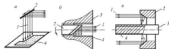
Схемы нагрева изделий под закалку с помощью лазера: а – поверхность цилиндрического изделия; б – внутренняя поверхность отверстия; в – жароустойчивость цилиндрического изделия; 1 – лазерный луч; 2 – маска; 3 – деталь; 4 – зона закалки
